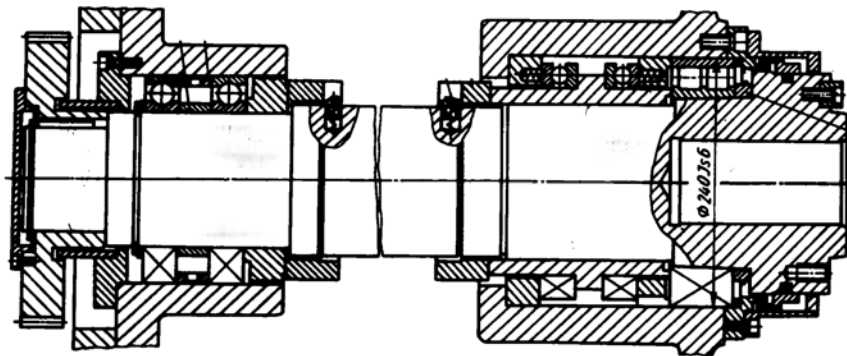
Шпиндельный узел расточной бабки агрегатного станка
